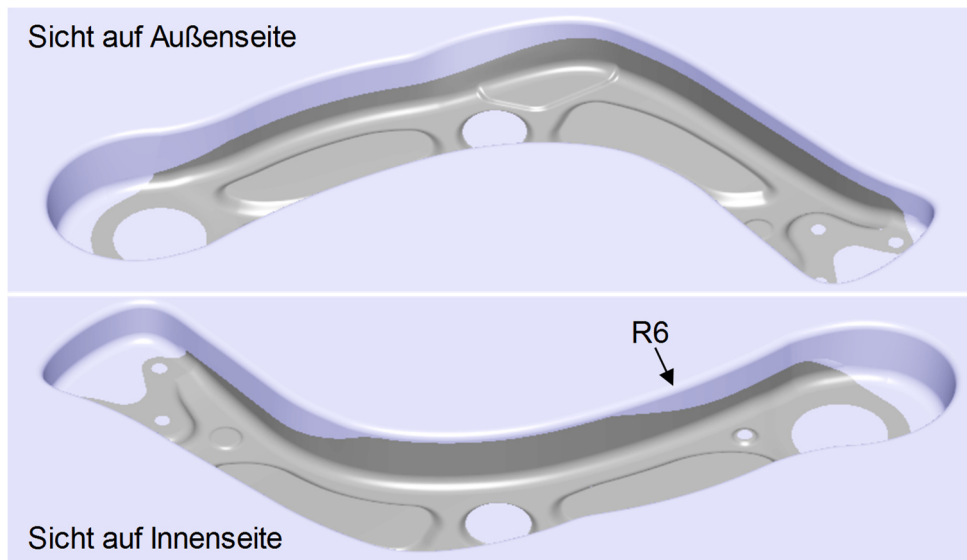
Ziehanlage des Querlenker-Werkzeugs mit umlaufend konstantem Radius
